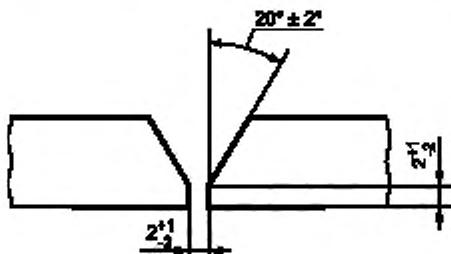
Конструктивные элементы подготовки кромок под сварку
